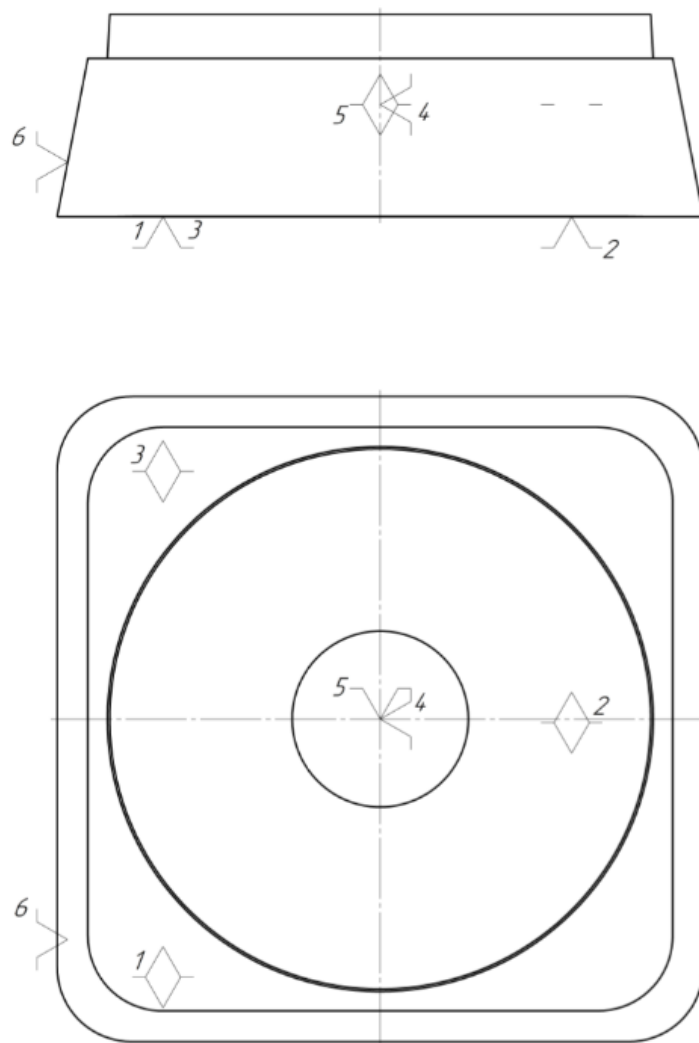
Схема базування деталі «Корпус» по ТБ 2.
